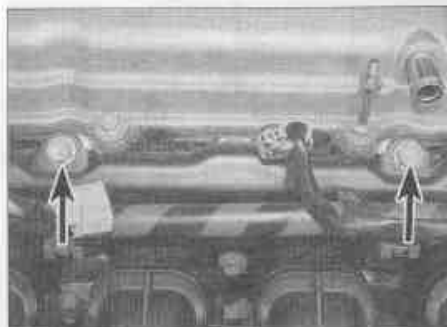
Выверните два болта крепления топливной рамы (отмечены стрелками)
